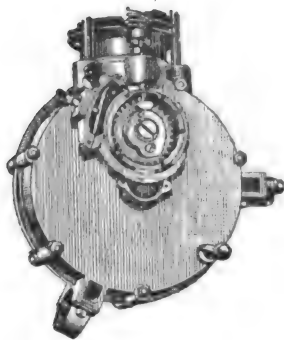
Zündungs- und Auspuffventilsteuerung zum Motorzweirad von Schild & Co.
